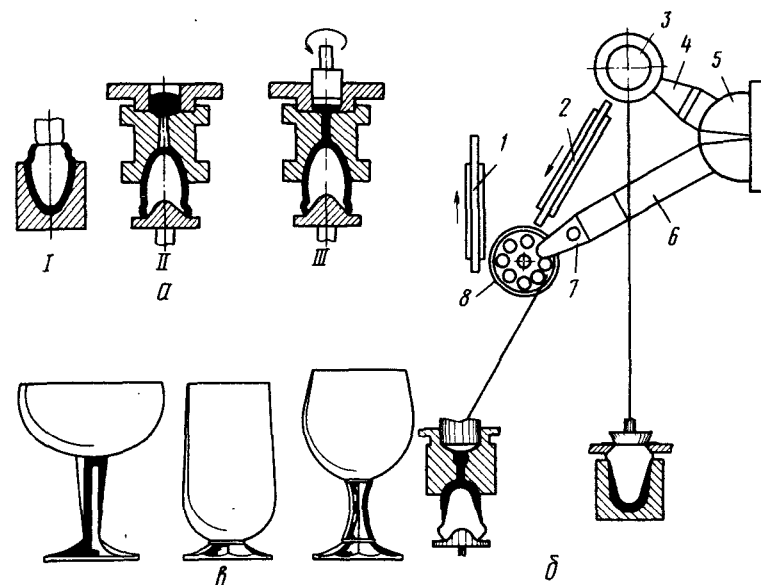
Схемы изготовления изделий на ножке (*а*), технологической линии для получения изделий с цветной ножкой (*б*) и виды вырабатываемых изделий (*в*)
